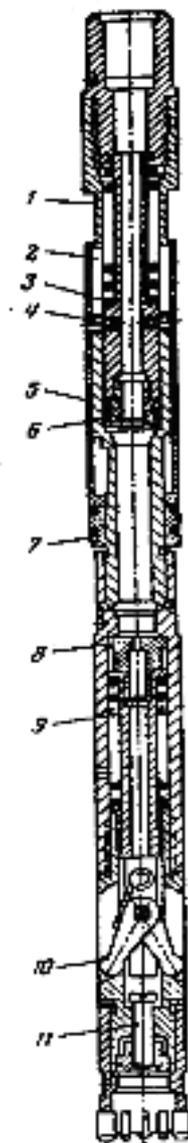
Труборез-труболовка: 1 – корпус труболовки; 2 – пазы; 3 – пружина труболовки; 4 – штифт; 5 – гильза; 6 – поршень труболовки; 7 – плашк; 8 – поршень трубореза; 9 – пружина; 10 – резцы; 11 – винт
